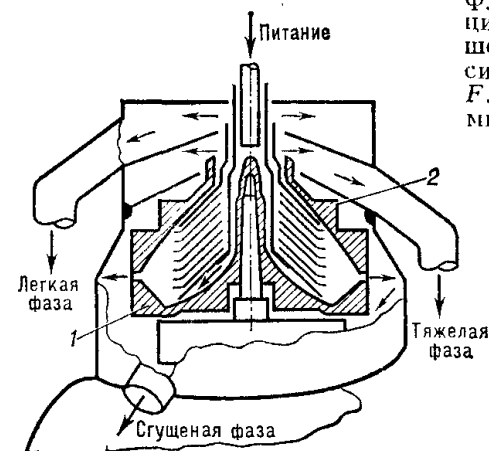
Центрифуга с гидравлич. выгрузкой осадка: 1 — сопло; 2 — ротор с пакетом тарелок.
